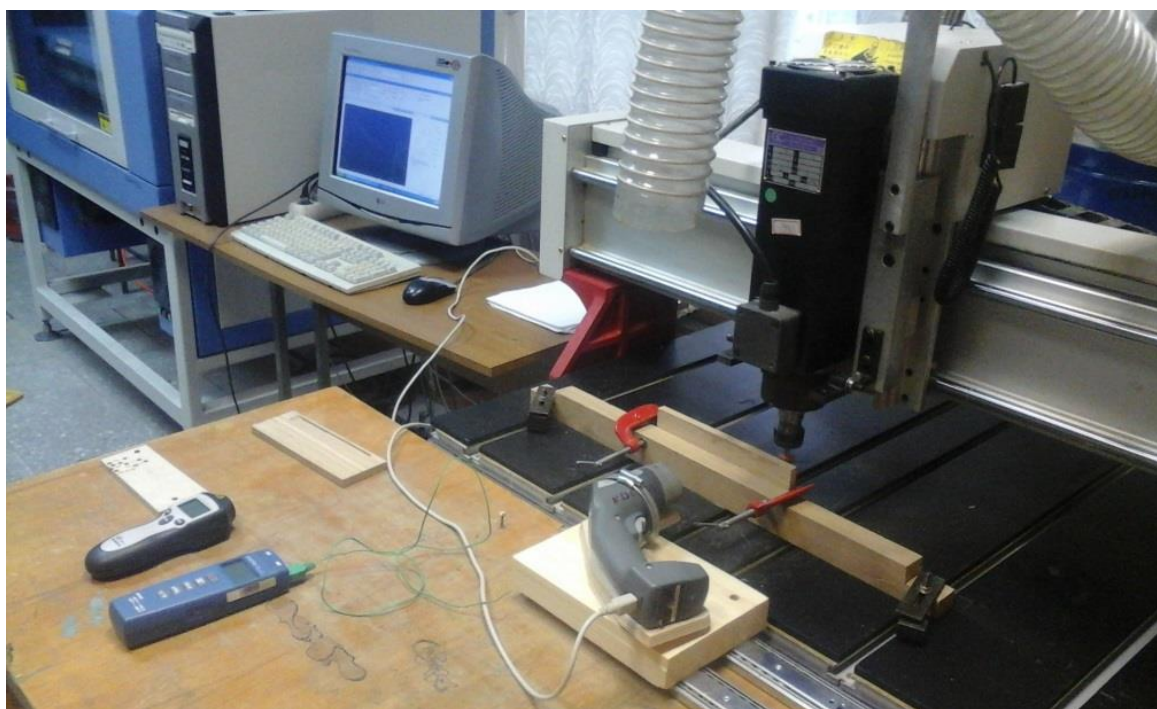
Экспериментальная установка на базе фрезерного станка с ЧПУ Beaver 9A
